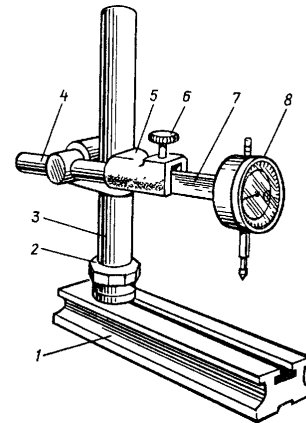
Індикаторний штатив 1 - основа; 2 - стопорна гайка; 3 - колонка; 4 - висувна штанга; 5 - рухома колодка; 6 - гвинт; 7 - подовжувач; 8 - індикаторна головка
